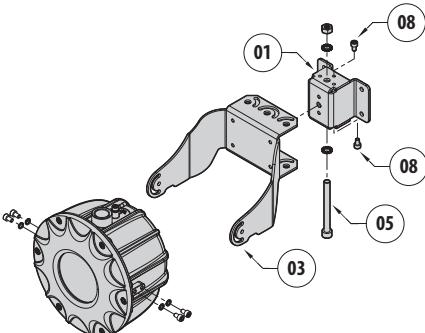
Fixation sur mur avec entrée des câbles dirigée vers le haut.
